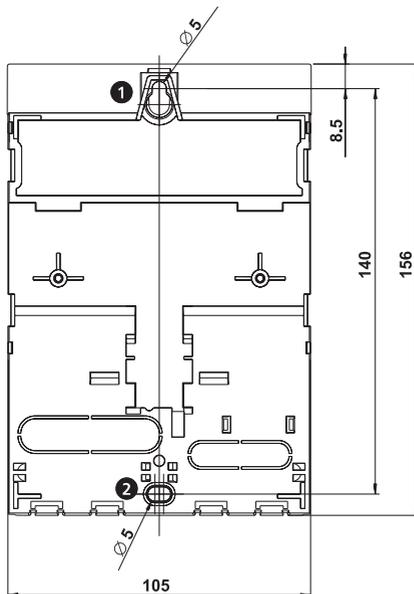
Rückseite des Reglers mit Montageöffnungen oben ❶ und unten ❷
